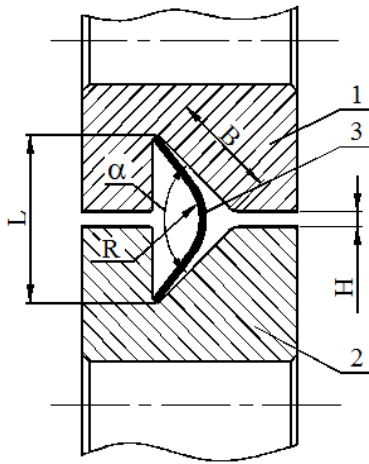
Роликовый калибр для формовки углового профиля осадкой: 1 – верхний ролик; 2 – нижний ролик; 3 – заготовка
